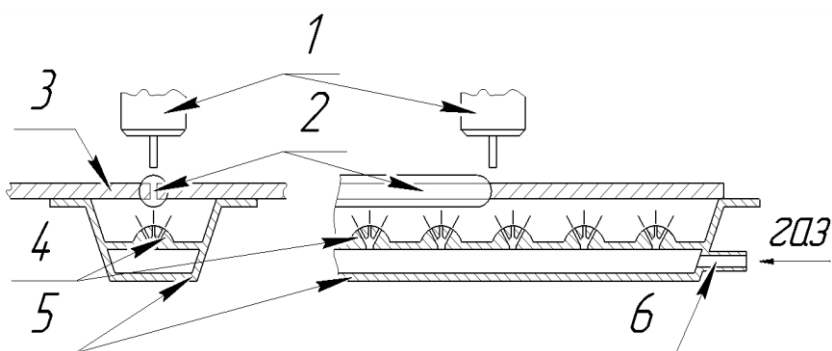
Пример устройства, обдувающего изделие газом: 1 – сварочная головка; 2 – сварной шов; 3 – свариваемые детали; 4 – форсунка, 5 – корпус охладителя; 6 – питающая трубка
